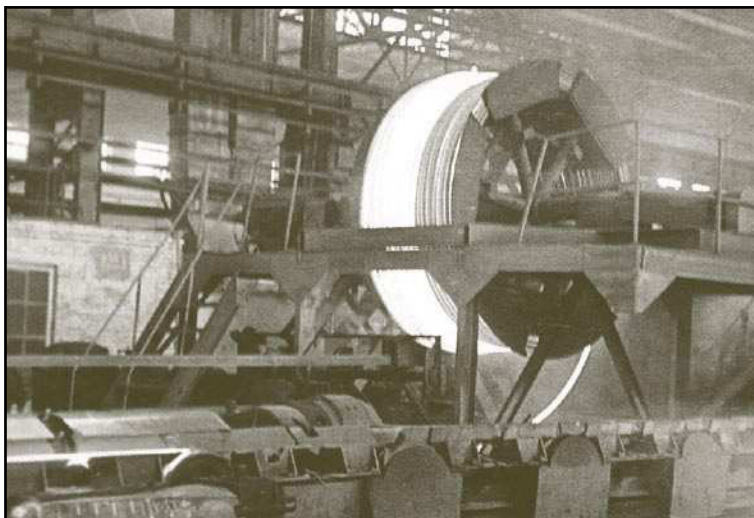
Установка для смотки непрерывной горячей трубы на барабан
